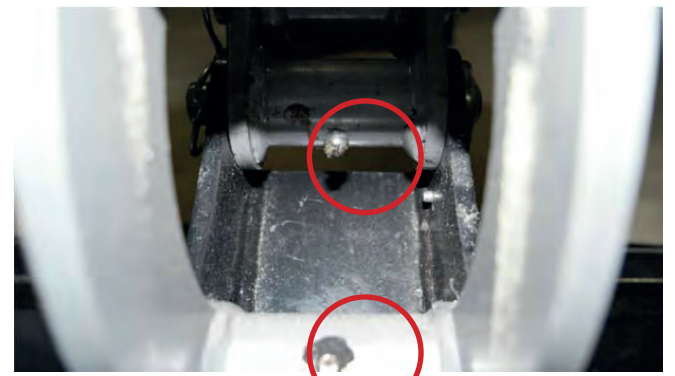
Tornillo de lubricación acoplador de cuchara 1
